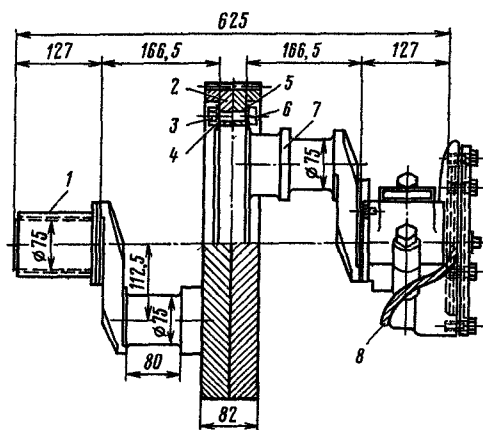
Коленчатый вал компрессора Э-500: 1 — подшипник, 2 — венец шестерни, 3 — болт; 4 — шайба, 5 — замковая шайба, 6 — гайки, 7 — коленчатый вал, 8 — корпус компрессора
